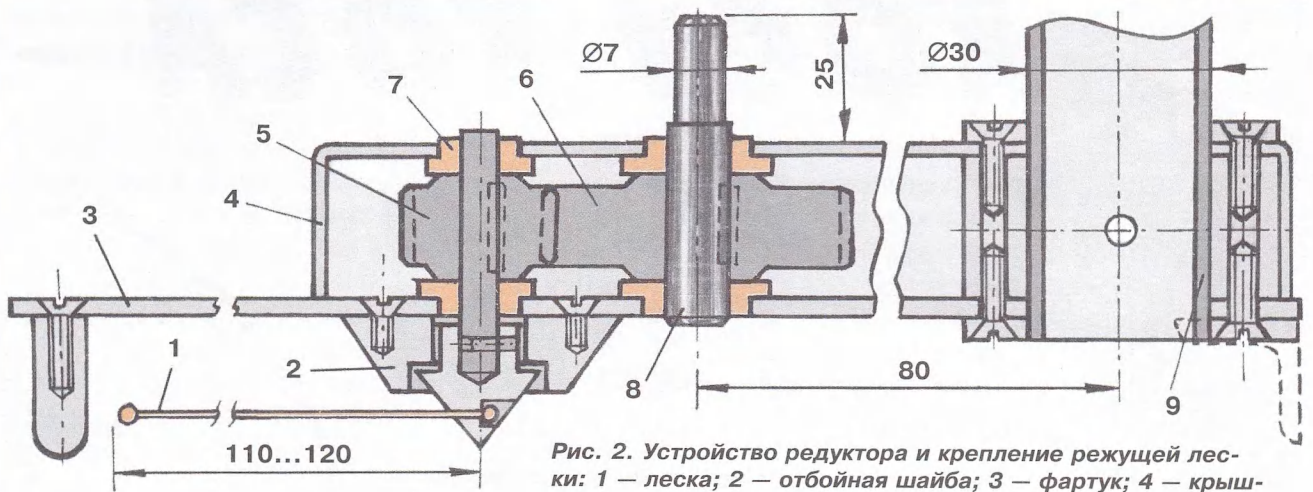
Устройство редуктора и крепление режущей лески: 1 – леска; 2 – отбойная шайба; 3 – фартук; 4 – крышка; 5 – ведомая шестеренка; 6 – ведущая шестеренка; 7 – втулка; 8 – ведущий вал; 9 – опорная часть штанги.
